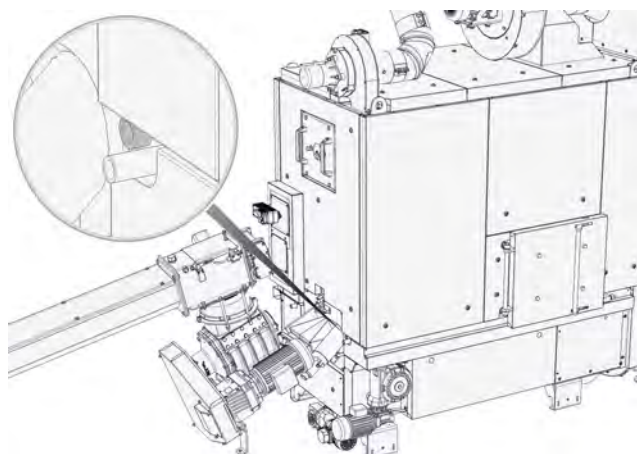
Raccord pour sonde de température de la soupape thermique de la chambre de combustion
